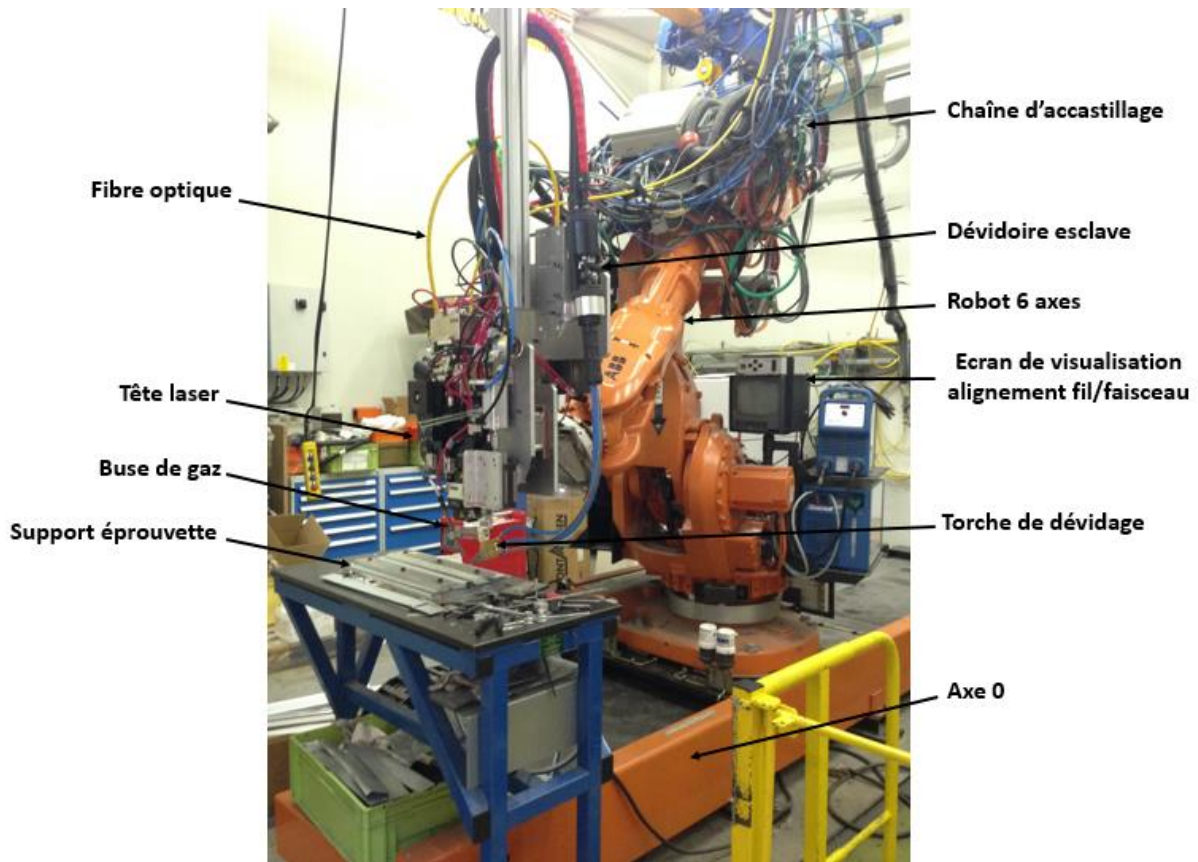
Vue de face du moyen robotisé et du support éprouvette.
